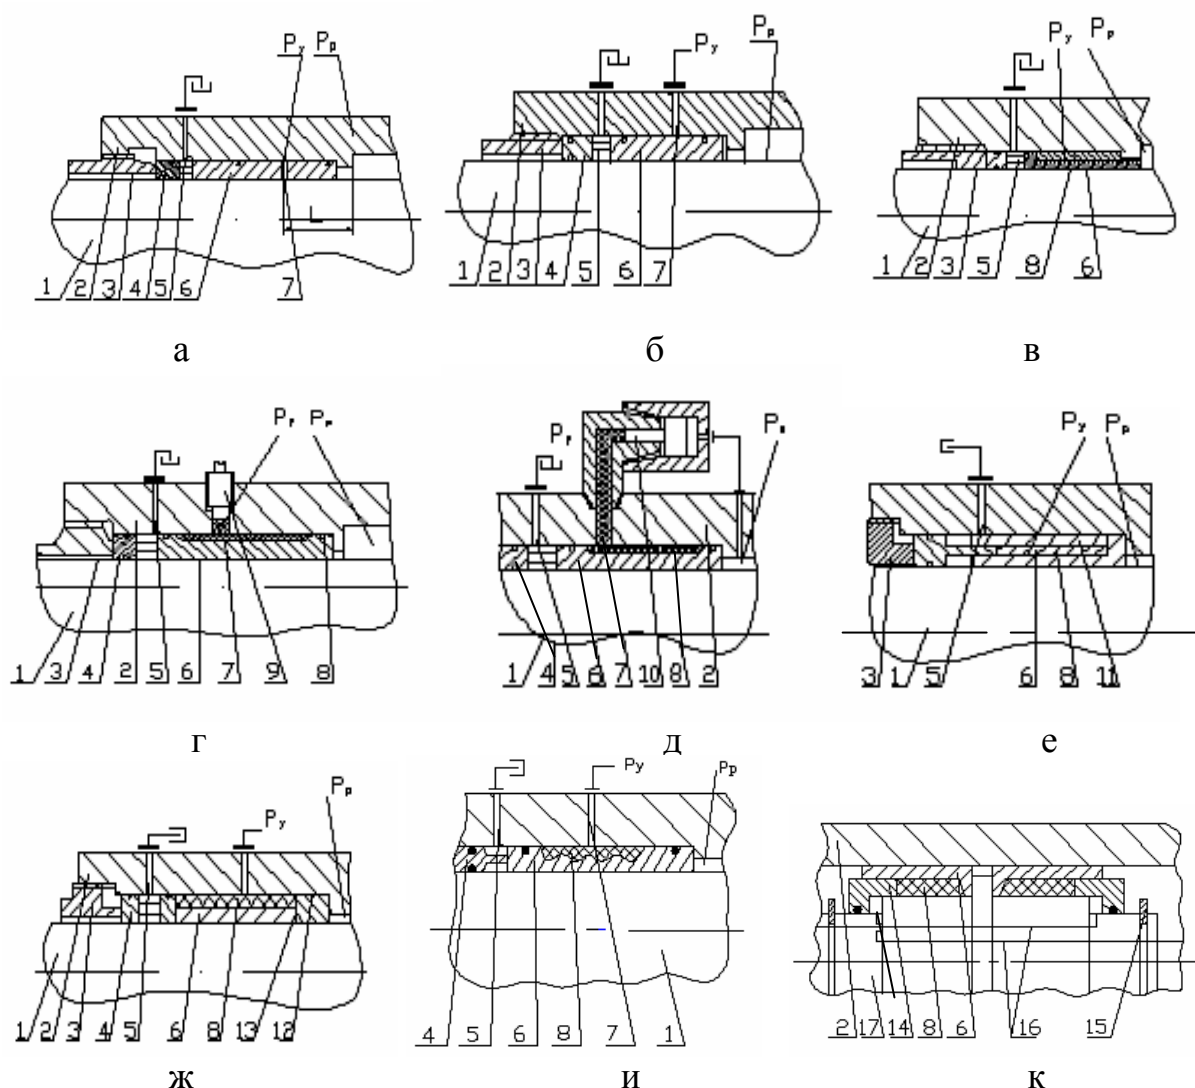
Конструктивные схемы направляющих с регулированием зазора в щели созданием давления среды на поверхность втулки
